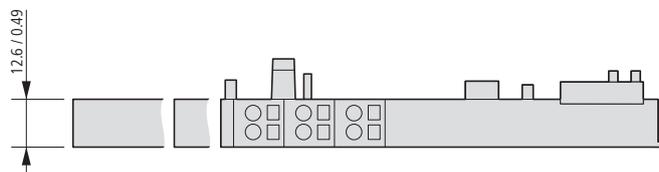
Draufsicht Basismodul in Scheibenausführung
